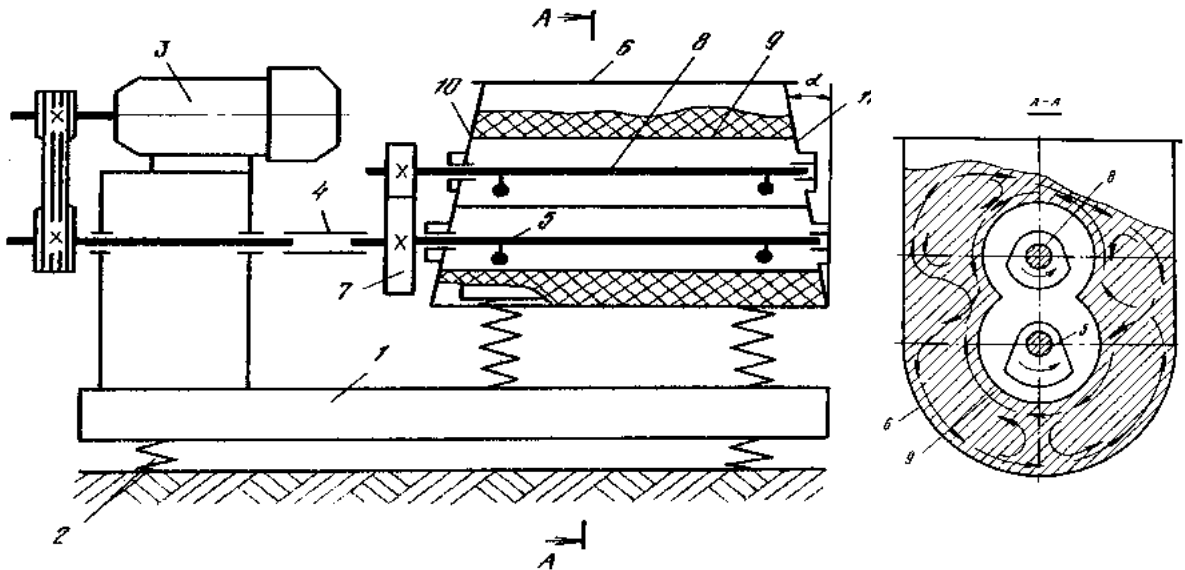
Двочастотний вібраційний пристрій: 1 – основа;
